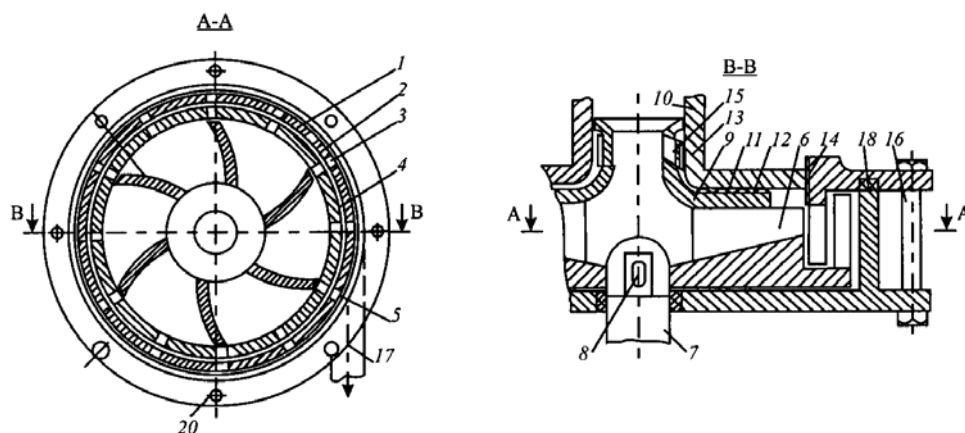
Роторно-пульсационный аппарат для диспергирования волокнистой суспензии концентрацией 0,5 ... 2,0 %: 1 – статор; 2 – корпус; 3, 5 – прорезы статора и ротора; 4 – ротор; 6 – клиновидные лопасти; 7 – вал; 8 – шпонка; 9 – насадка; 10 – входной патрубков; 11 – кольцевой канал; 12 – рифления на стенках ротора и статора; 13 – горловинообразная часть статора; 14 – резьба; 15 – направляющие отверстия; 16 – болты; 17 – выходной патрубков; 18 – прокладка; 19 – лапы; 20 – отверстия для крепления
